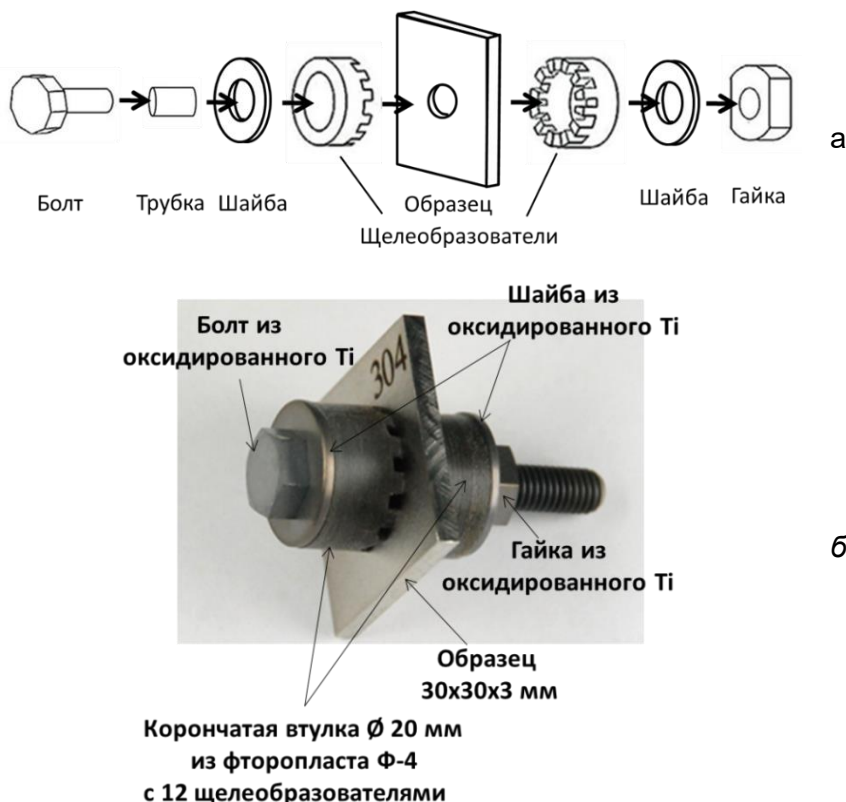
Порядок сборки (а) и внешний вид контактной пары «металл-неметалл» (б) для испытаний образцов стали 316L на склонность к ЩК по стандарту ASTM G-78-01
